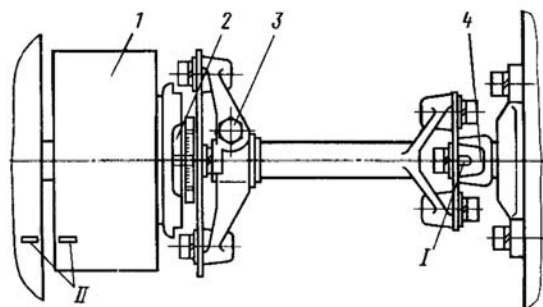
Установка начала впрыска топлива в первом цилиндре двигателя по меткам: 1 — автоматическая муфта опережения впрыска; 2 — полумуфта ведомая; 3 — стяжной болт; 4 — задний фланец ведущей полумуфты; I, II — метки
